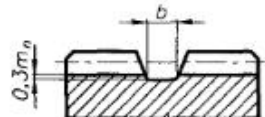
Размеры канавок для выхода червячных фрез
